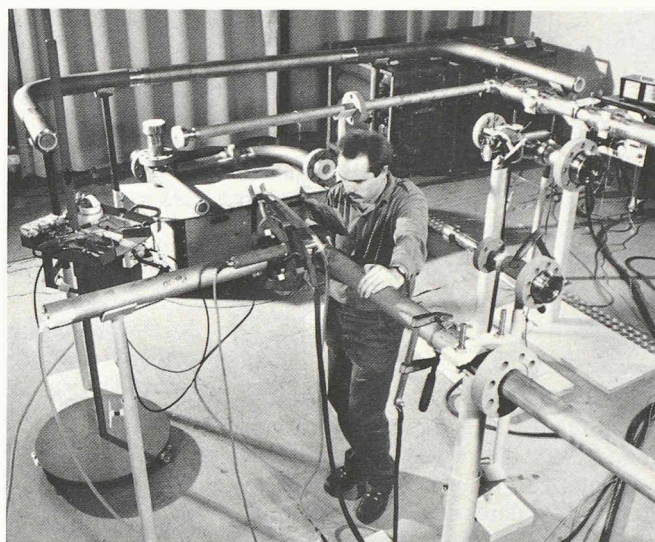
Machine à souder orbitale semi-automatique pour le soudage des tubes.
